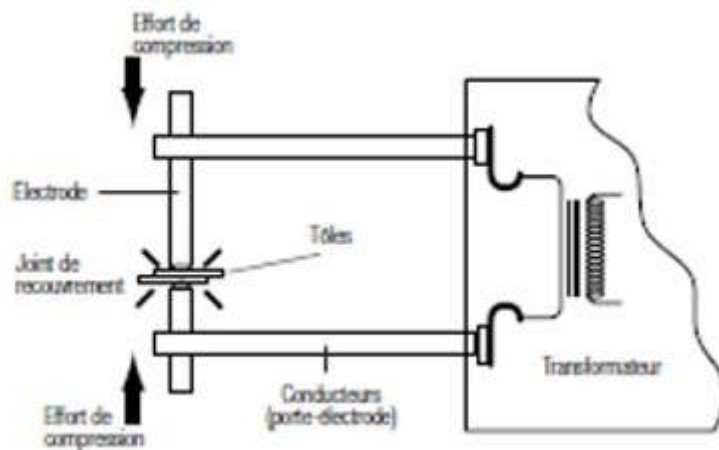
Principe de procédé de Soudage par point[17]
